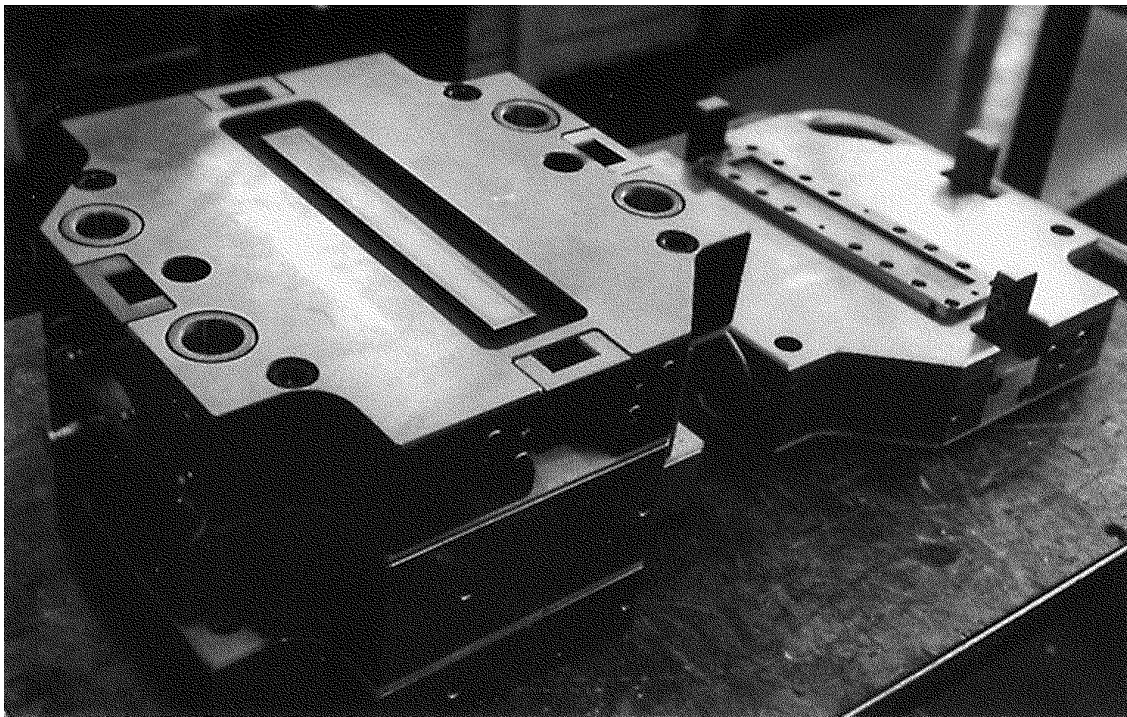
Heißprägewerkzeug mit großer Kavität, geöffnet
